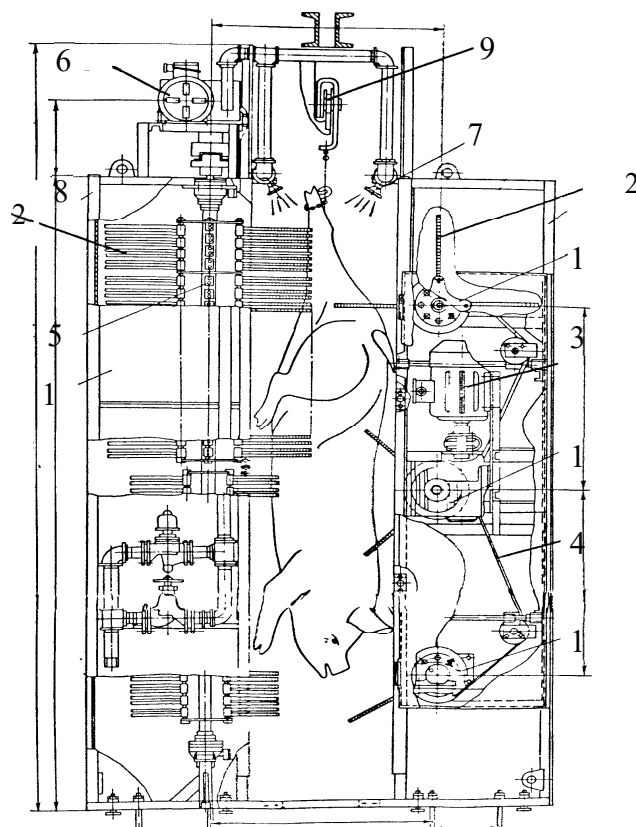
Миина машина К /-ФМД: 1 – горизонтальний барабан; 2 – гумові били; 3 – привод; 4 – клинопасова передача; 5 – вертикальний барабан; 6 – привод; 7 – пристрій для зрошування; 8 – захисні стінки; 9 – підвісний конвеєр.
